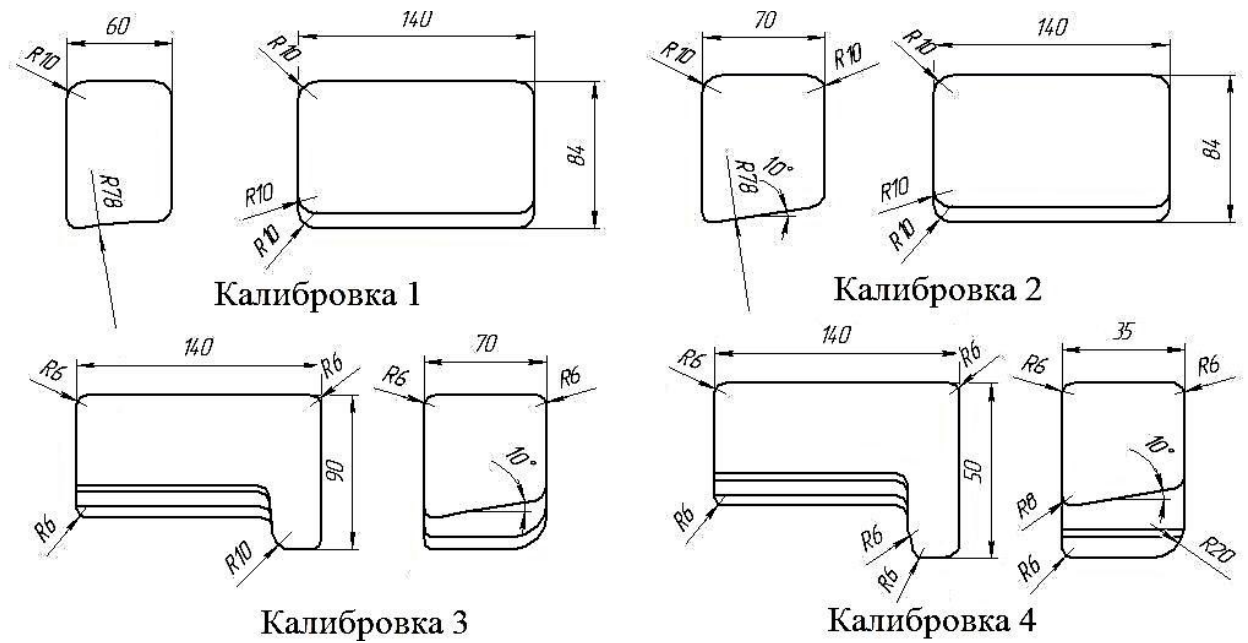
Виды калибровок бойков для обжатия конца заготовки
